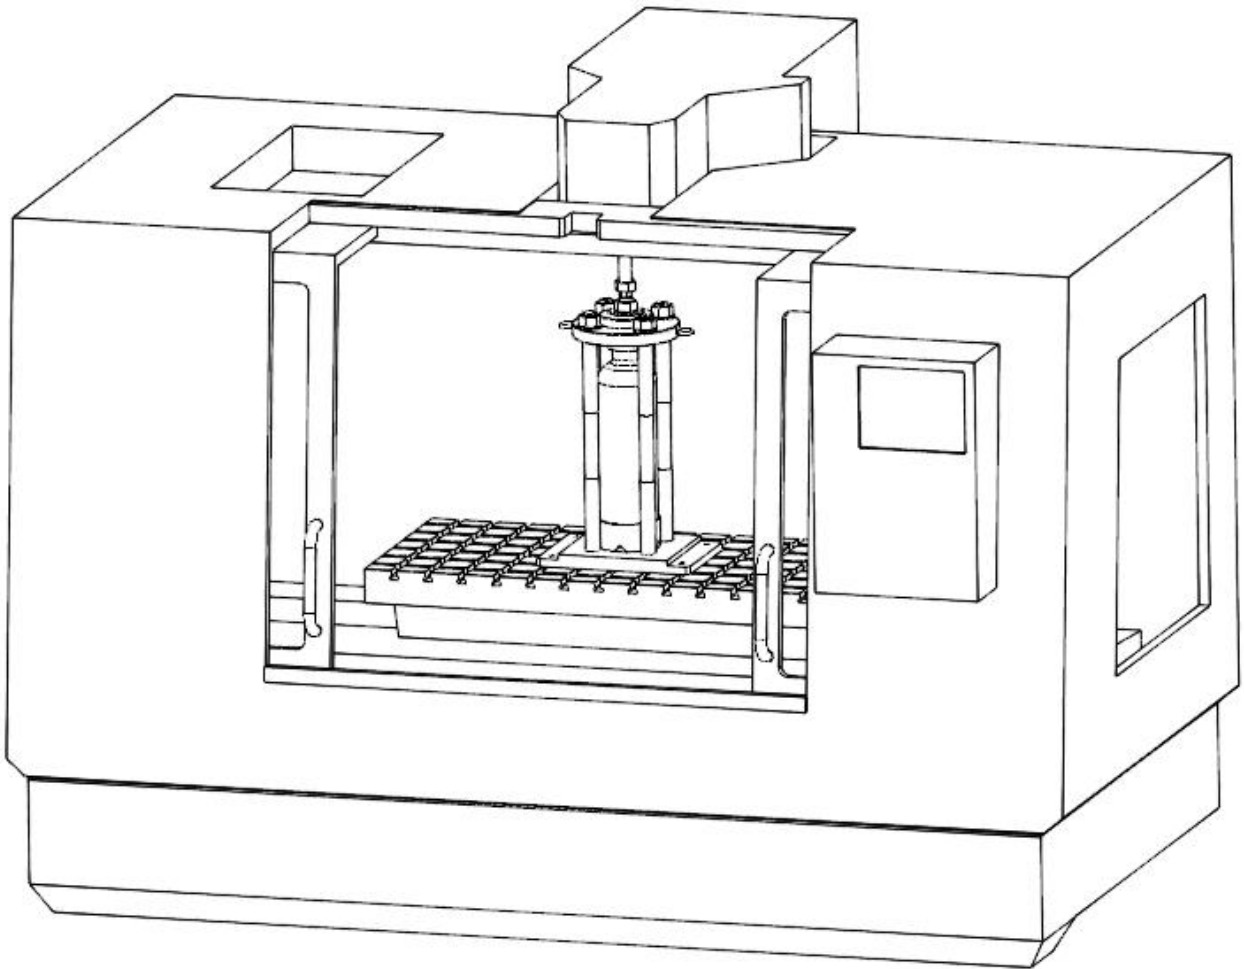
Встановлений пристрій на випробувальний стенд
